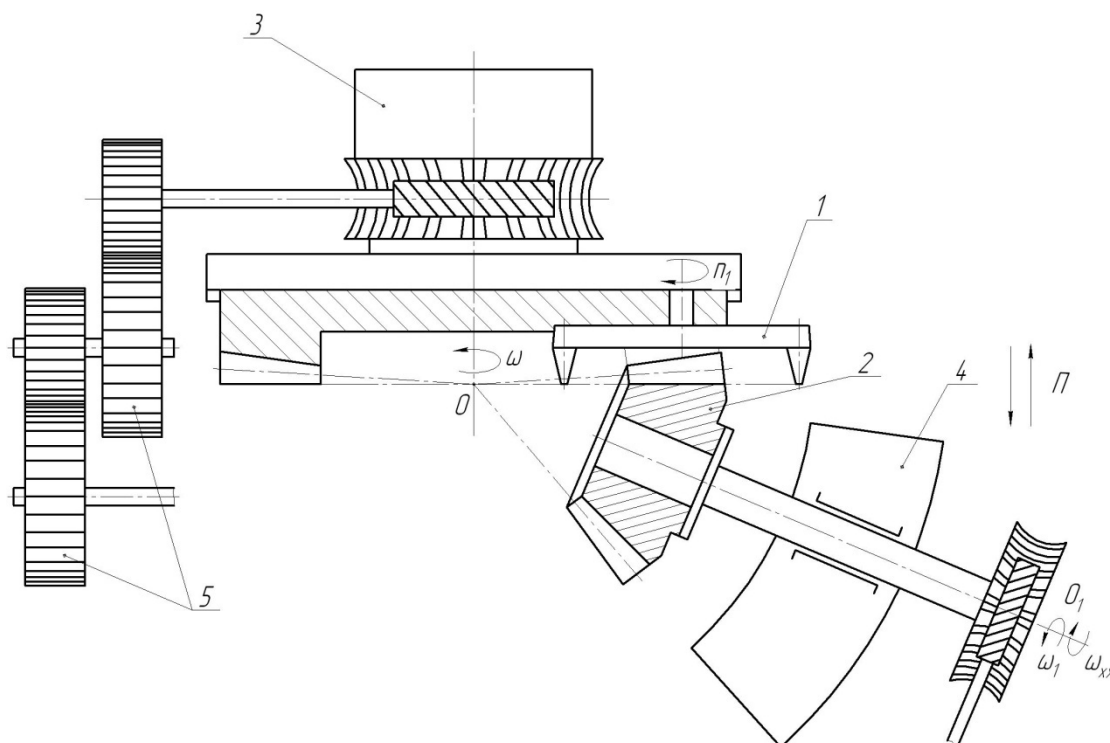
Принципиальная схема нарезания конических колес с круговыми зубьями по методу обкатки: 1 – резцовая головка; 2 – нарезаемое коническое колесо; 3 – плоское колесо (воображаемое); 4 – поворотный стол; 5 – сменные шестерни.
